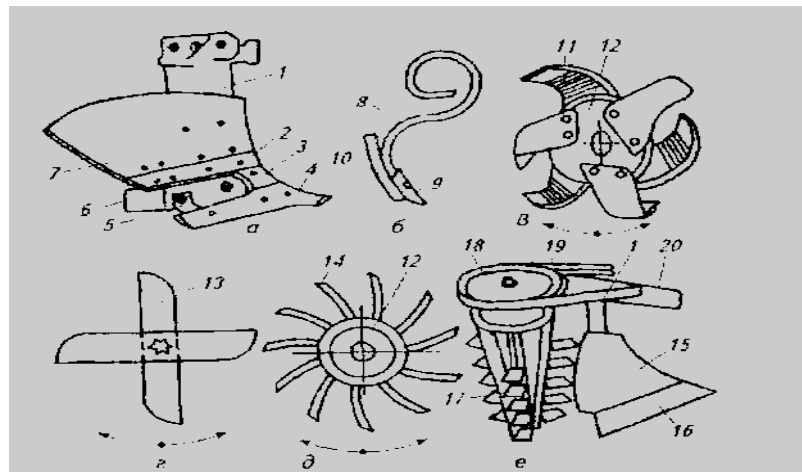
Комбіновані робочі органи: а – вирізний корпус плуга; б – розпушувальний зуб-сошник; в – фреза; г – хрестоподібні ножі; д – голчастий диск; е – корпус плуга-фрези; 1 – стійка корпусу; 2 – верхній леміш; 3 – шиток; 4 – нижній леміш; 5 – розпірка; 6 – польова дошка; 7 – відвал; 8 – розпушувальний зуб; 9 – лапа; 10 – патрубок підведення насіння (добрив); 11 – ніж; 12 – диск; 13 – двосторонній ніж; 14 – голка (палець); 15 – груди відвалу; 16 – леміш; 17 – ножовий барабан; 18 – шків; 19 – приводний ремінь; 20 – рама плуга.
